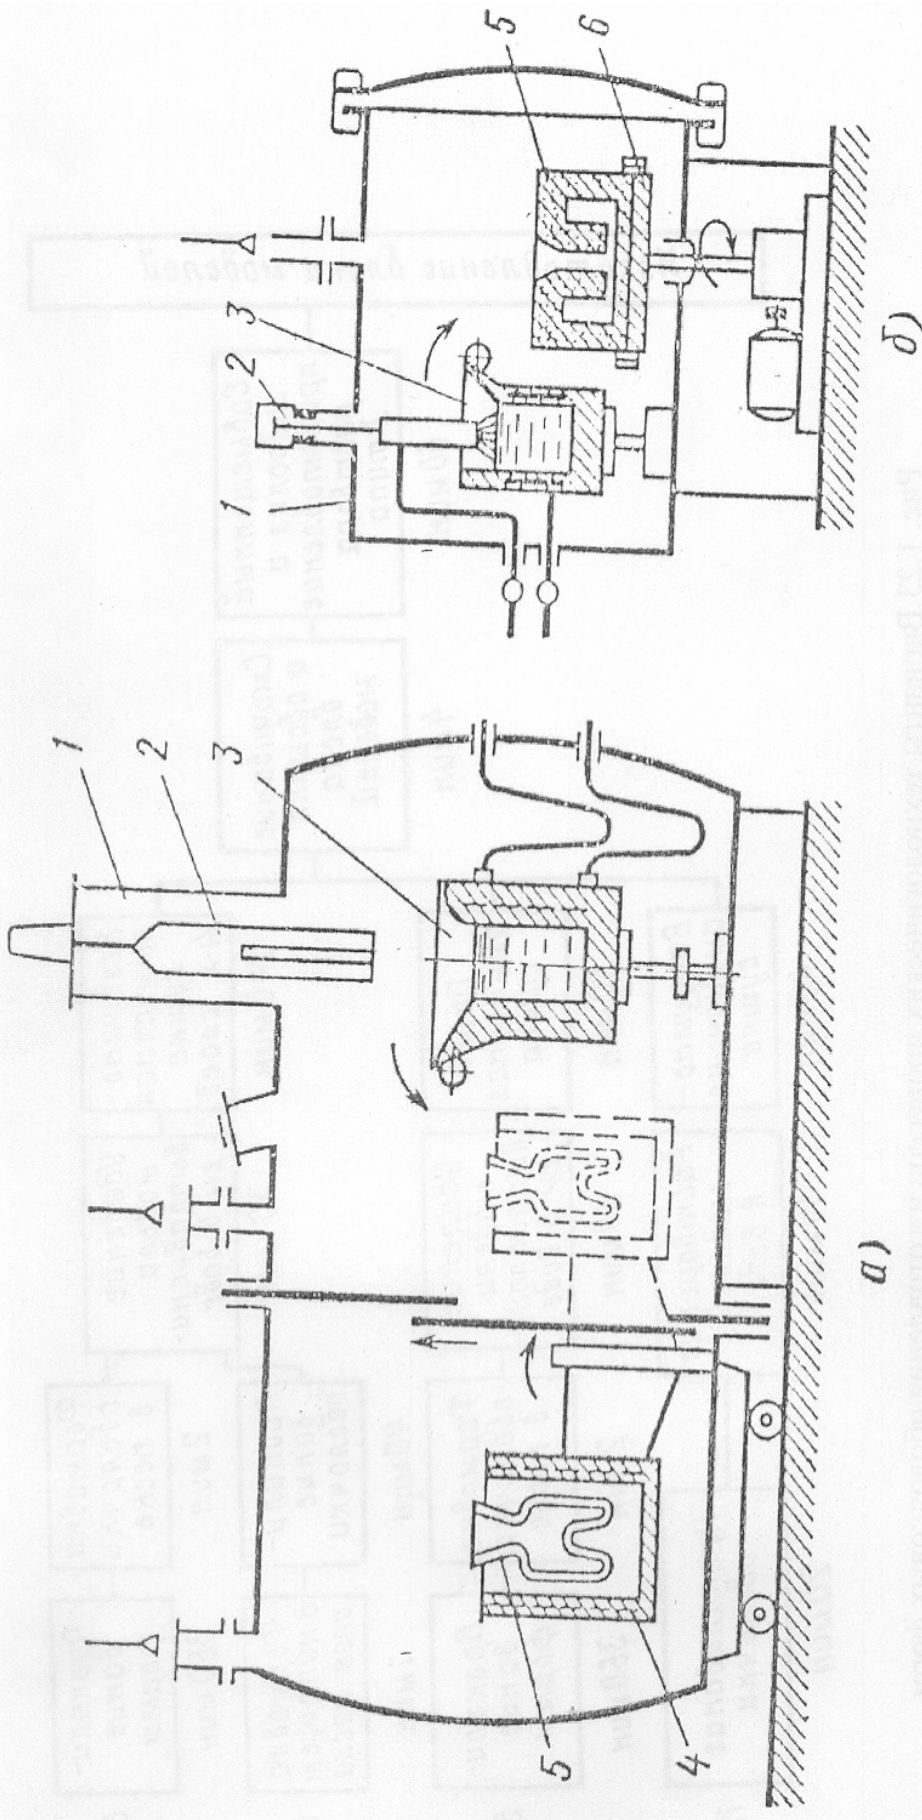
Схемы устройства вакуумных плавильно-заливочных установок: а – с печью подогрева форм; б – с центробежной машиной; 1 – вакуумная камера; 2 – вакуумная камера; 2 – устройство для загрузки шихты; 3 – плавильная печь; 4 – печь подогрева; 5 – форма; 6 – центробежная машина.
